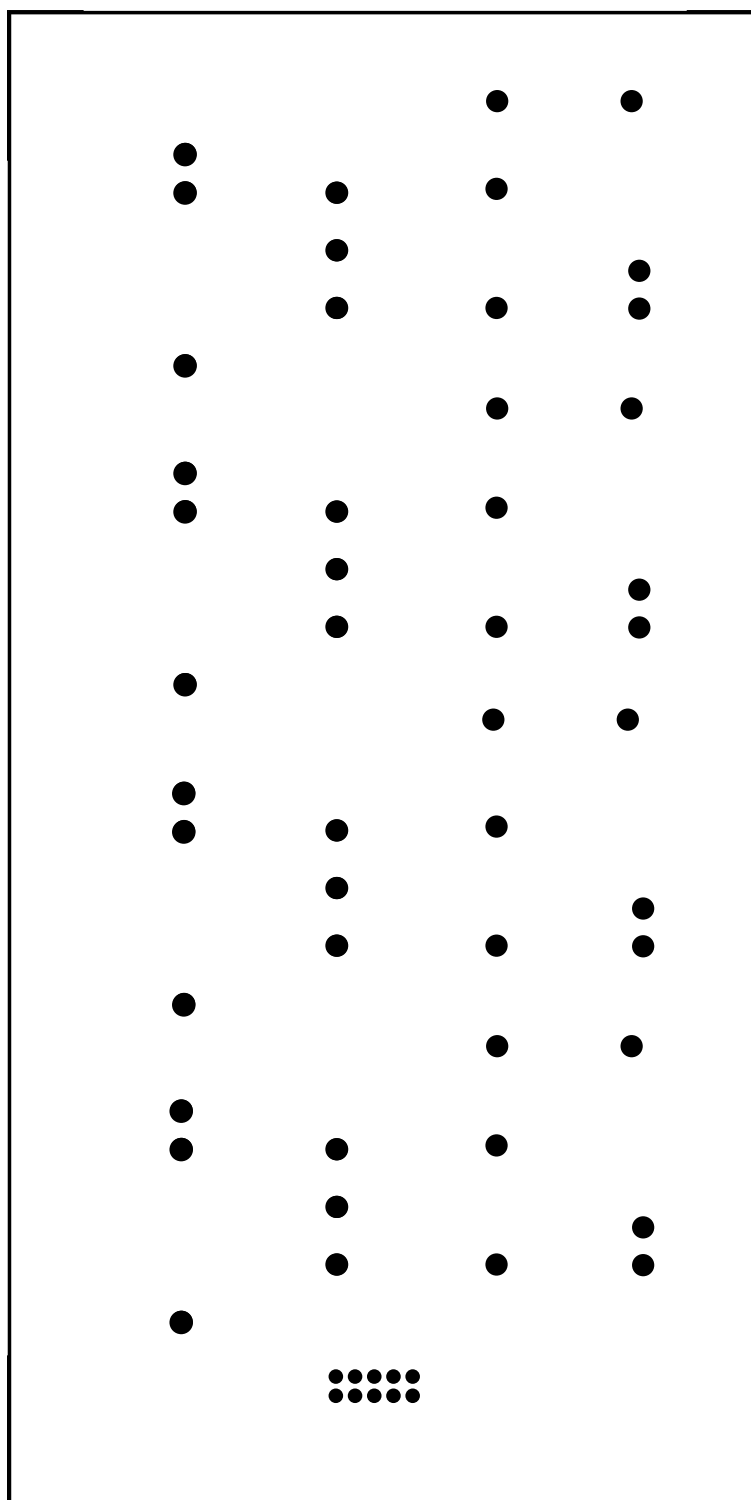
Máscara de solda da placa de sensores. Fonte: Própria.
